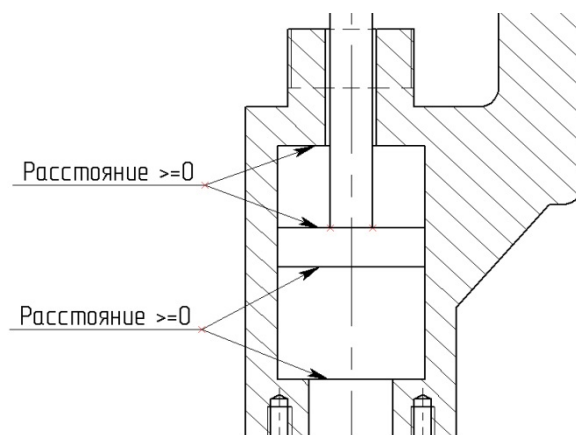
Сопряжение деталей «Корпус» и «Поршень»
